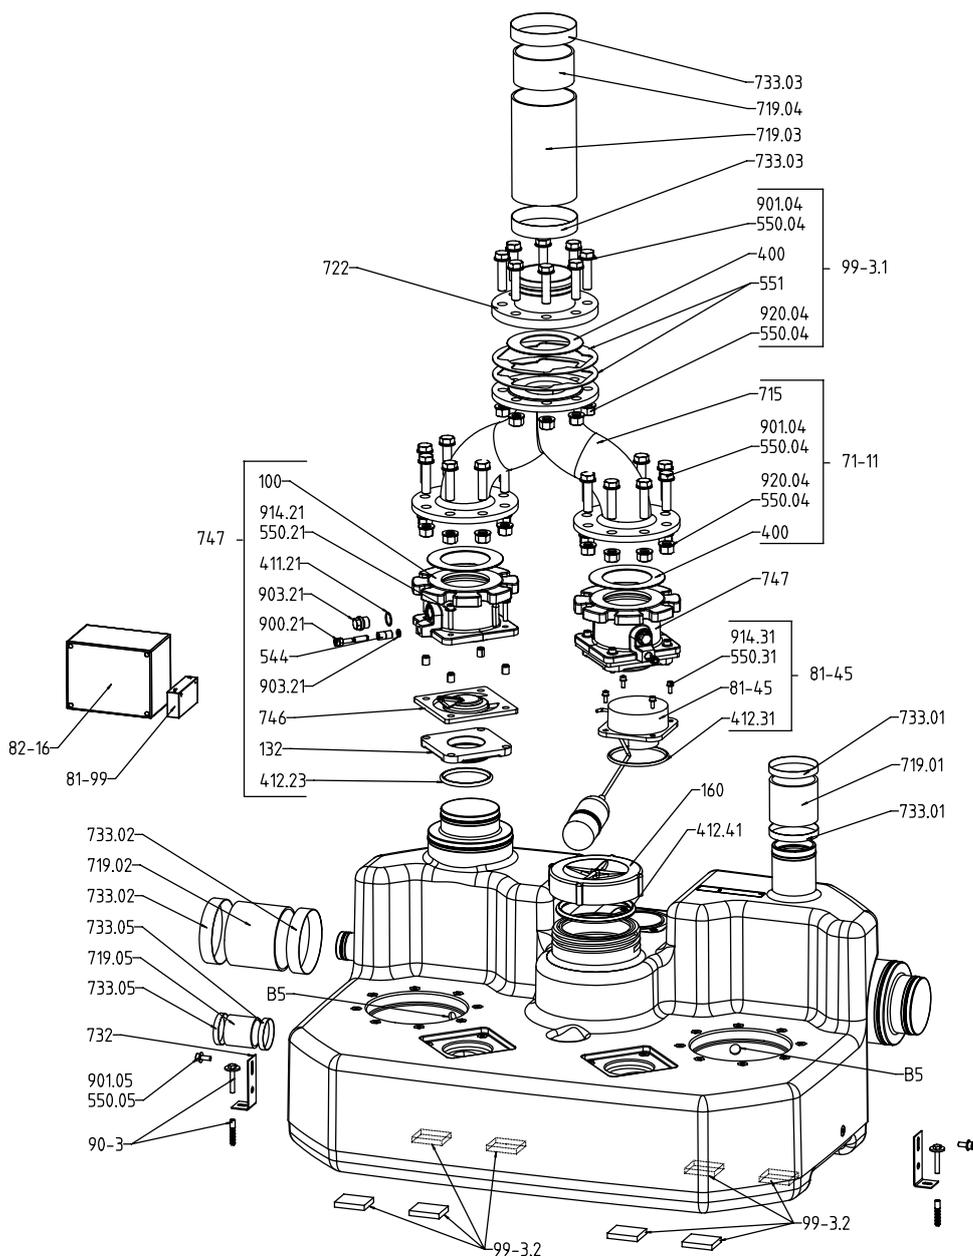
Детализированный чертеж mini-Компакта UZ150 - сборный резервуар
